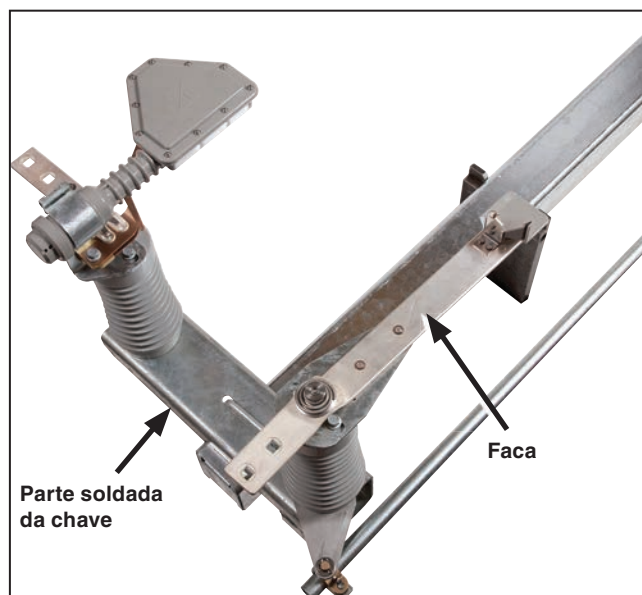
Faca a 90 graus da parte soldada da chave.
